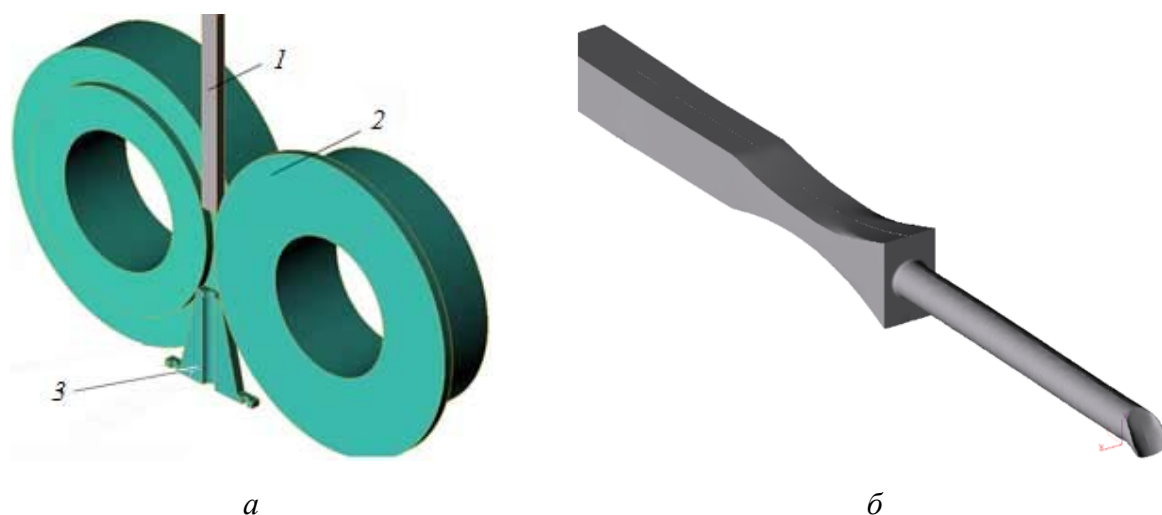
Схема процесса СПП (*а*) и профиль заготовки внутри очага деформации (*б*):
